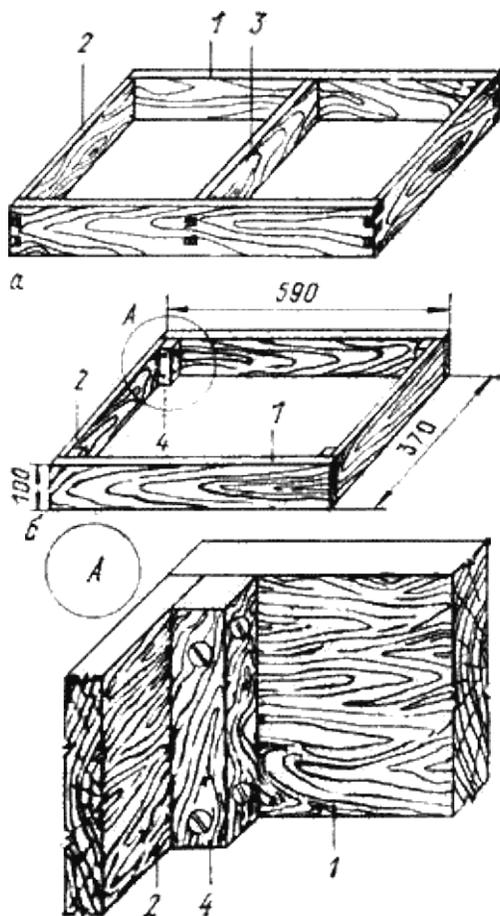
Цоколь: а — с шиповой вязкой; б — без шиповой вязки; 1 — продольная обвязка; 2 — поперечная обвязка; 3 — средник; 4 — соединительный брусок
